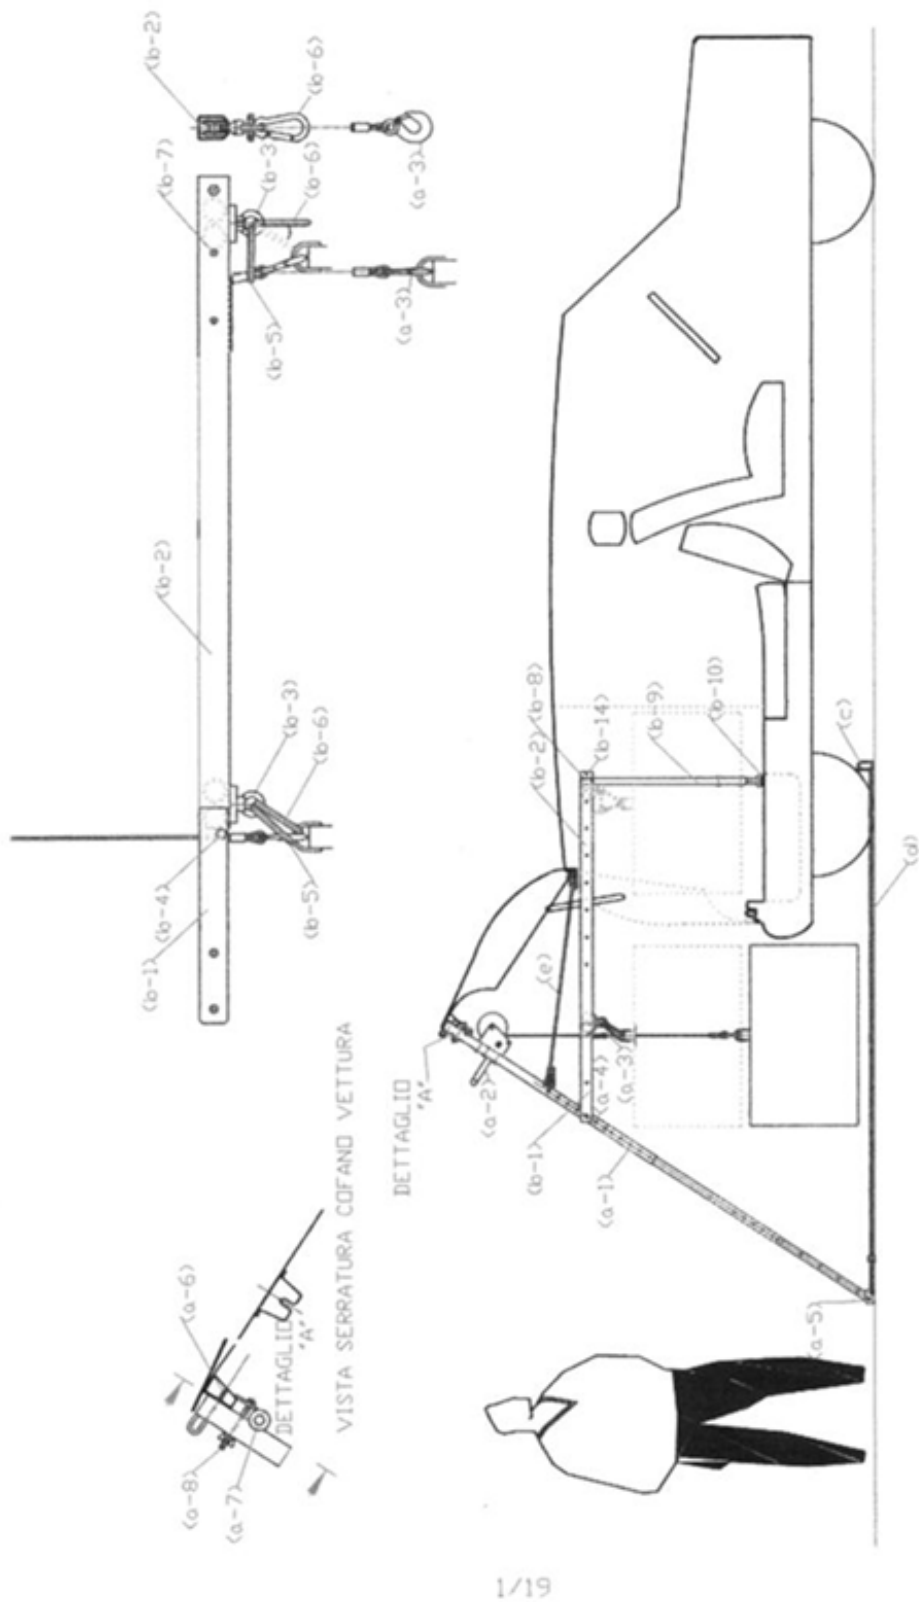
SEZIONE LONGITUDINALE SISTEMA DI CARICO VETTURA E PARTICOLARI
